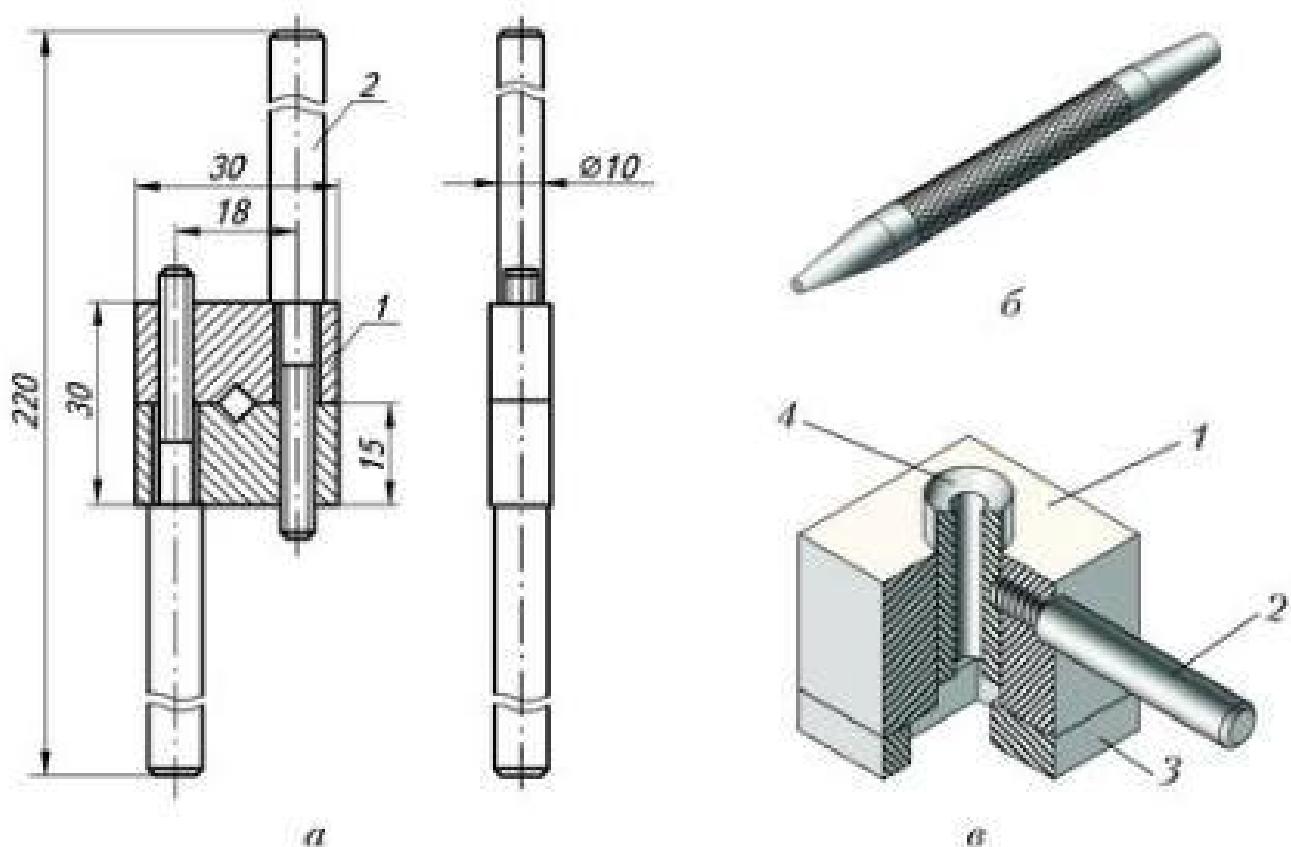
Способы представления изделий, выполненных на токарном и фрезерном станках: *а* – сборочный чертёж воротка; 1 – зажим; 2 – ручка; *б* – технический рисунок пробойника; *в* – технический рисунок кондуктора для сверления отверстий: 1 – корпус; 2 – ручка; 3 – основание; 4 – втулка
